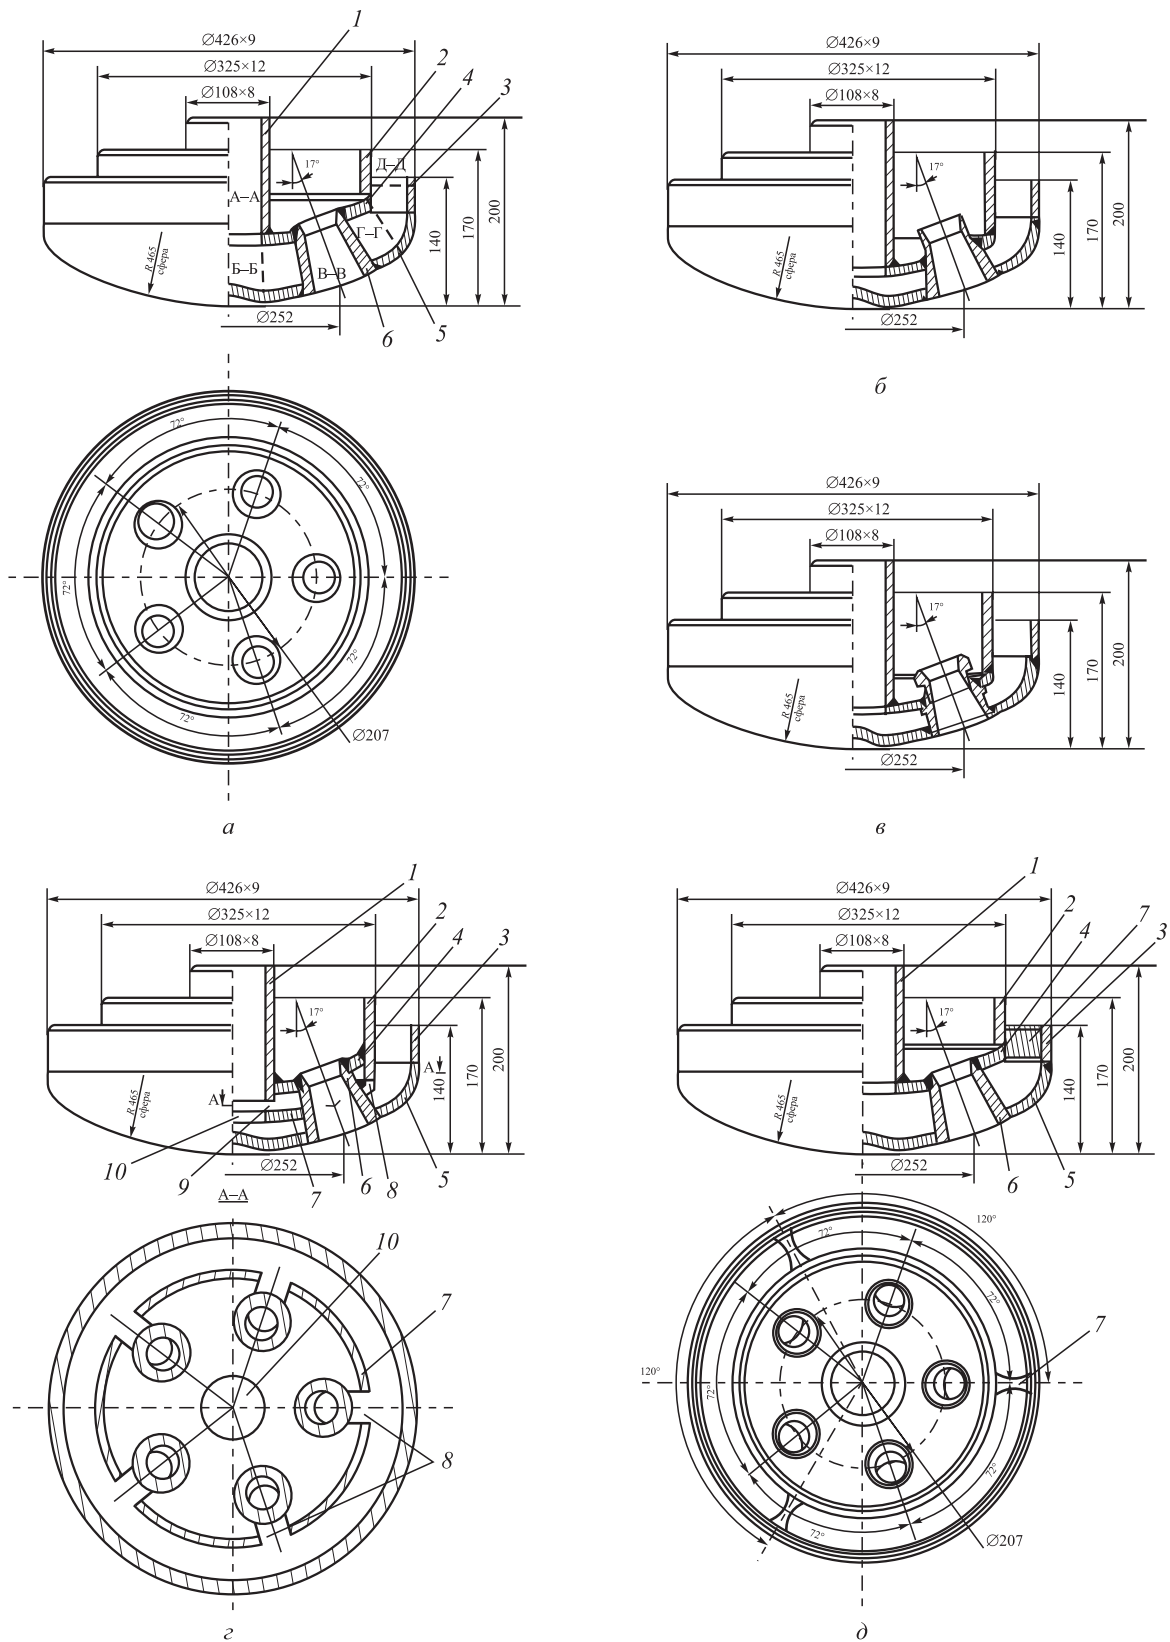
Сварные конструкции пятисопловых фурменных головок:
